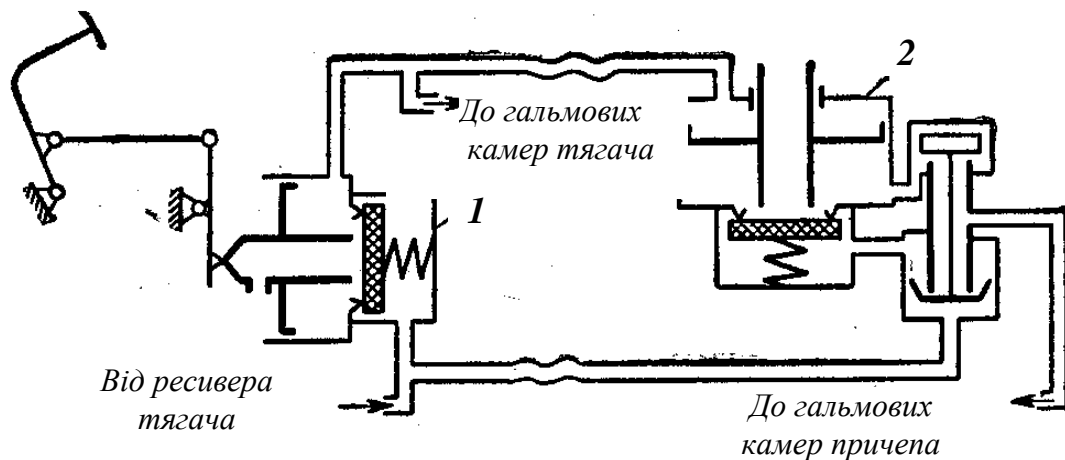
Принципова схема пневматичної двопровідної гальмової системи: 1 – гальмовий кран; 2 – прискорювально-аварійний клапан
